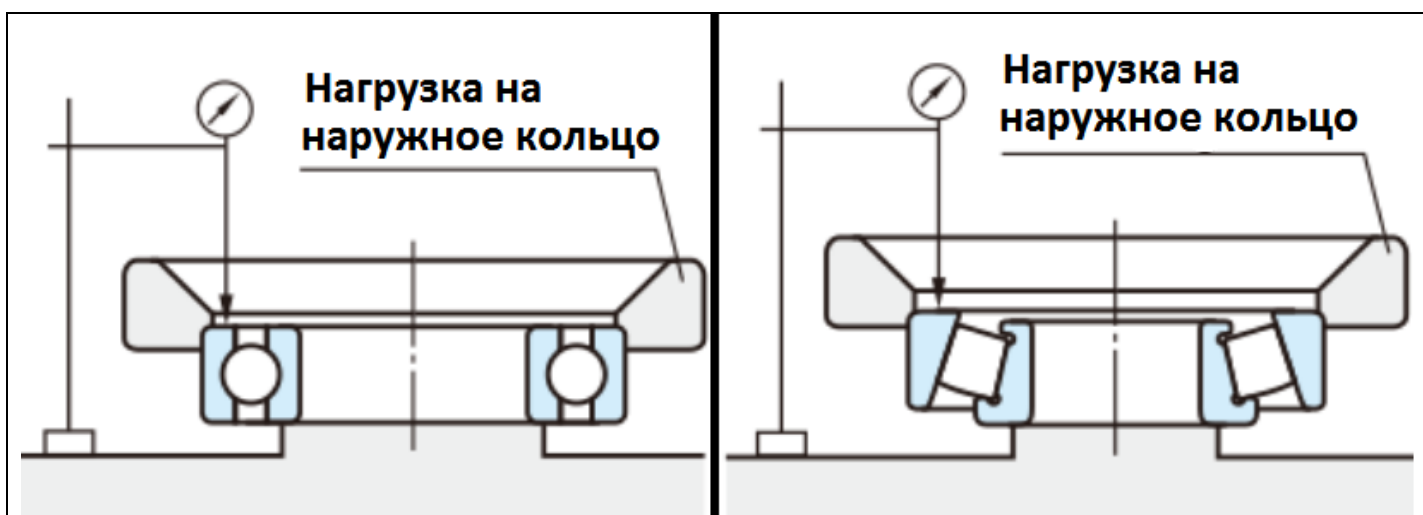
Торцевое биение наружного кольца подшипника в сборе. Наружное кольцо проворачивается на полный оборот.
